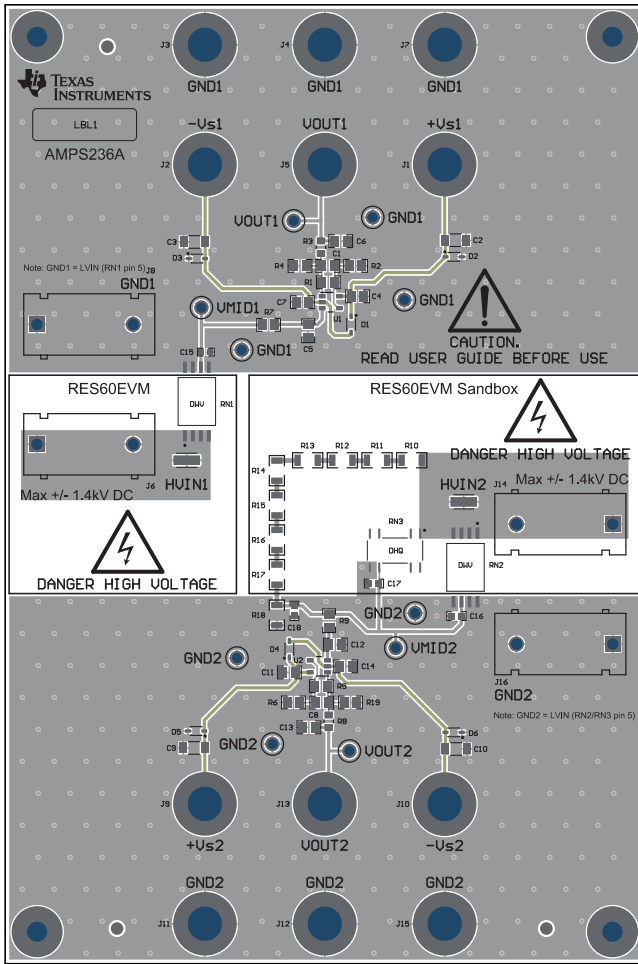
RES60EVM PCB 布局复合视图 (顶视图)
